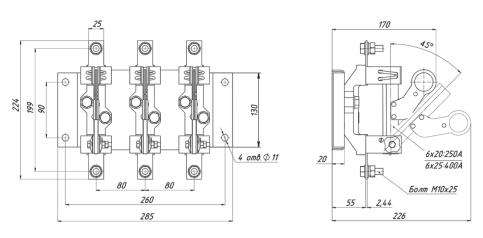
Разъединитель Р63 с пополюсным оперированием штангой ШО-1 на номинальный ток 630 A
